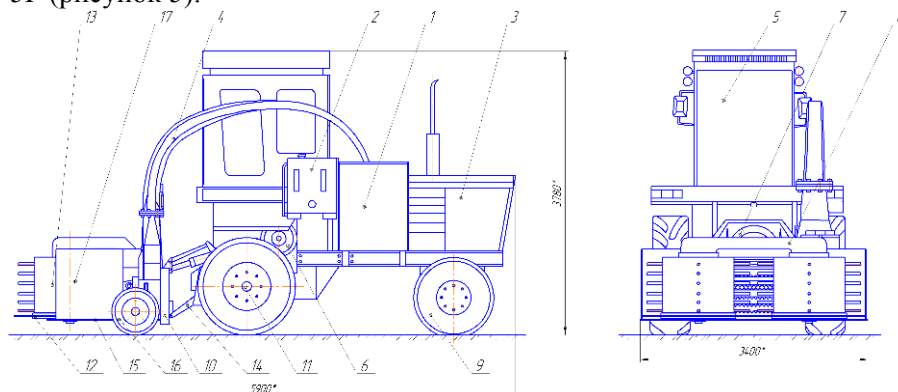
Машина для обрізки чагарників, навісна: 1 – бункер подрібненої маси; 2 – бак паливний; 3 – енергозасіб (КПС – 5Г); 4 – дефлектор; 5 – кабіна; 6 – кондпривод; 7 – подрібнювач; 8 – привод ножового апарату; 9 – поворотні колеса; 10 – привод подрібнювача; 11 – приводний міст; 12 – ножовий апарат; 13 – направляюча; 14 – навісний пристрій; 15 – рама машини; 16 – колесо опорне; 17 – щиток направляючий
